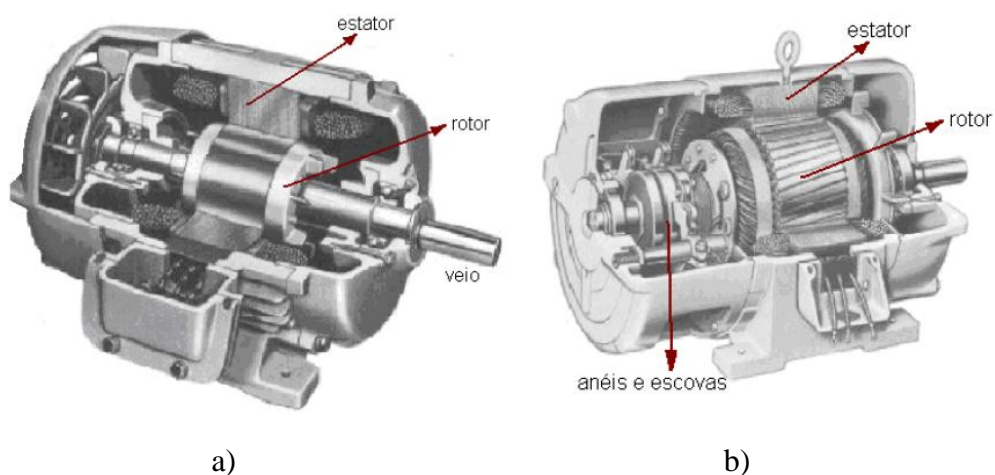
Corte de motor de indução com a) Rotor em gaiola de esquilo e b) Rotor bobinado.
